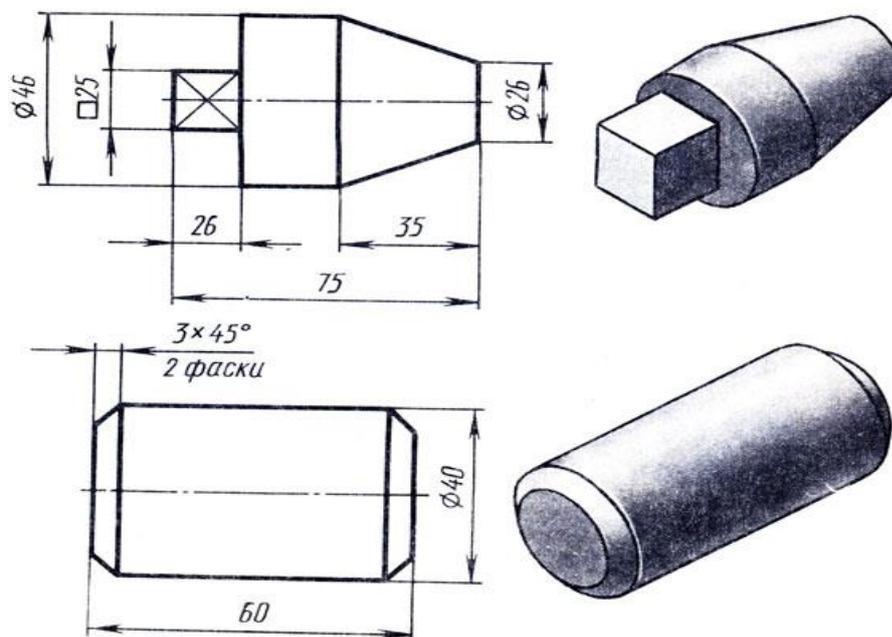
Детали, для выявления формы которых достаточно одного вида
